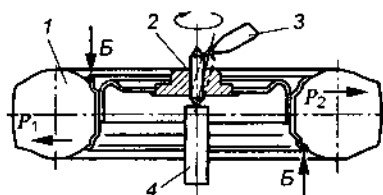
Динамическая балансировка колеса: 1 — колесо; 2 — приспособление; 3 — мел; 4 — опора
